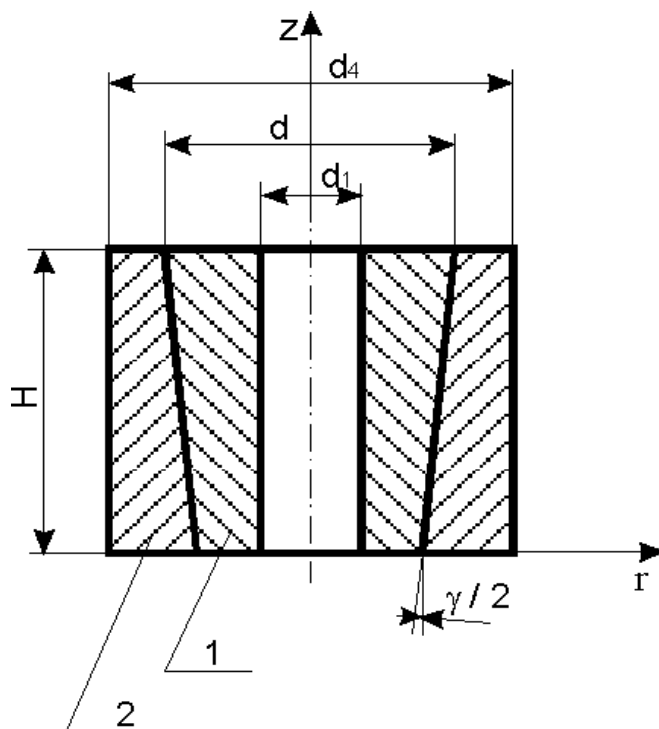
Схема сварного соединения с внешней обоймой
